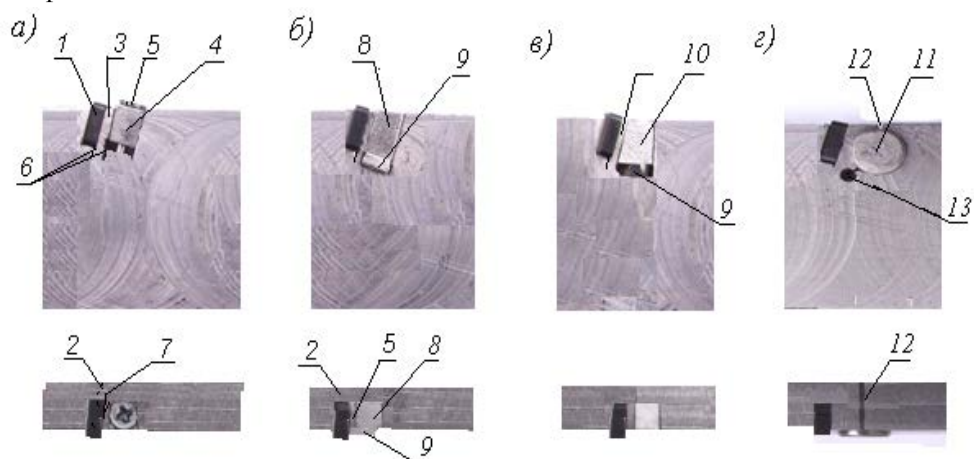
Крепление к корпусу кольцевой коронки пластин-резцов с хвостовиком типа «ласточкин хвост».
